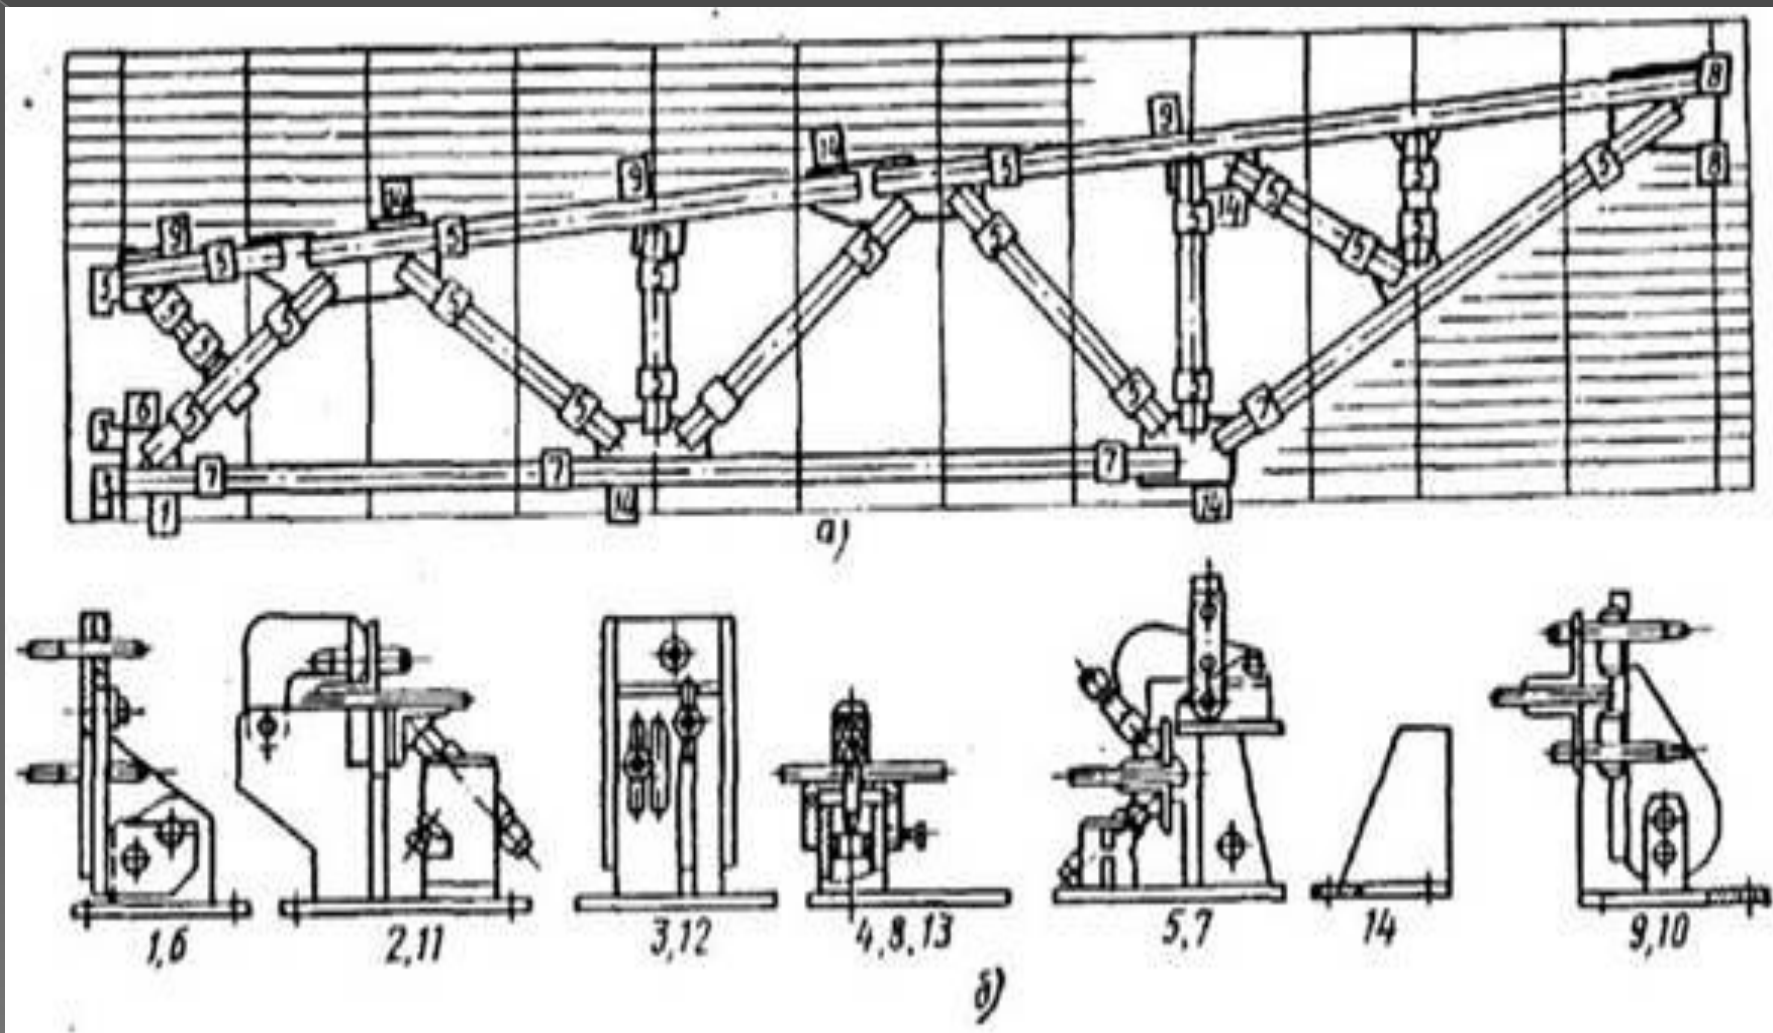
Кондуктор для ферм с применением универсальных сборочных приспособлений (УССП)
